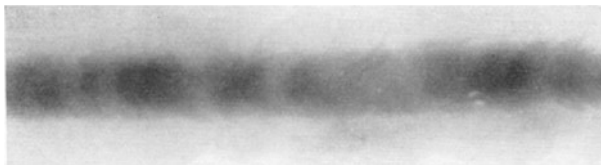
Röntgenaufnahme einer guten Elektroschweißung.
